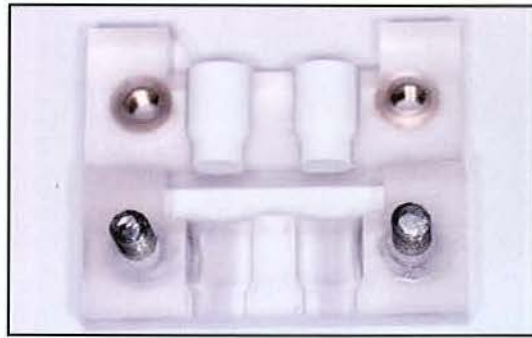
dispositivo bi-partido sob placa de gesso de revestimento alumina
